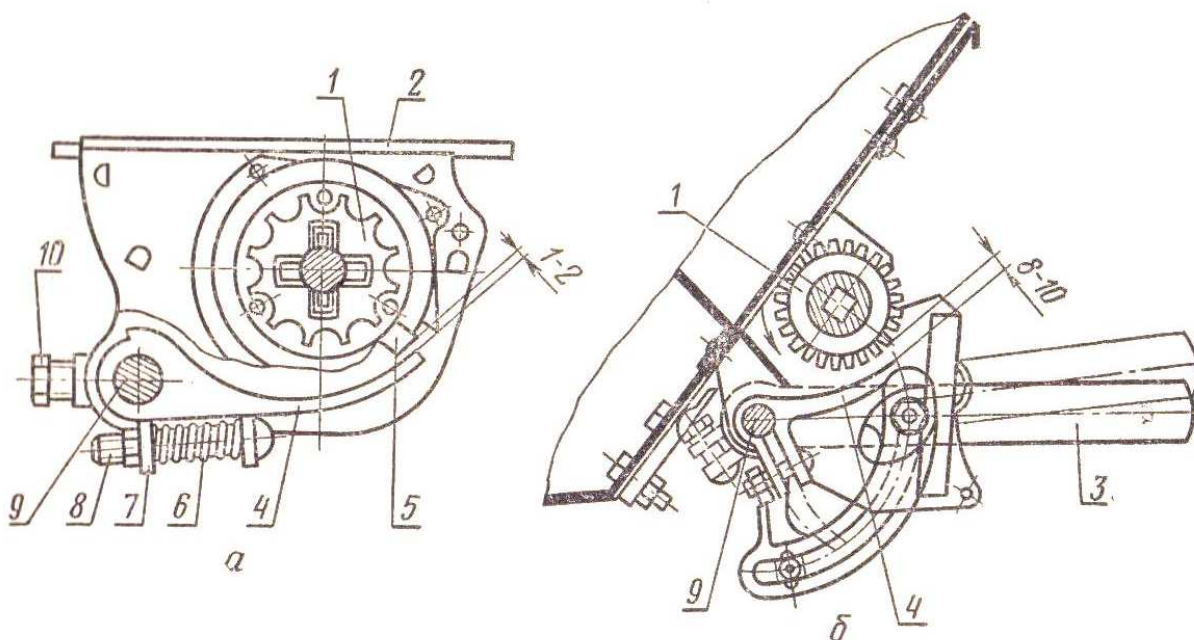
Высевающие аппараты зерновой сеялки СЗ-3,6: а – аппарат для семян; б – аппарат для высева гранулированных удобрений; 1 – катушка; 2 – коробка; 3 – рычаг вала клапанов; 4 – клапан; 5 – ребро муфты; 6 – пружина клапана; 7 – вставка клапана; 8 – болт; 9 – вал клапана; 10 – стопор
